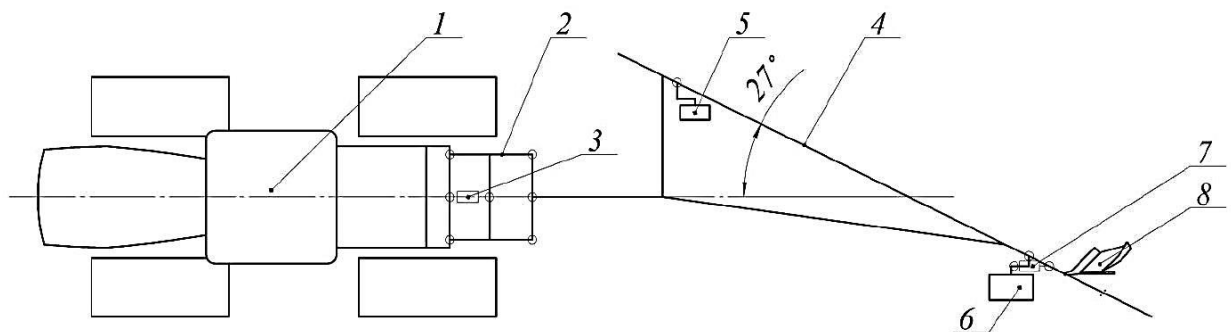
Принципова схема орного агрегату складається з широкозахватного навісного плуга загального призначення з класичними робочими органами
